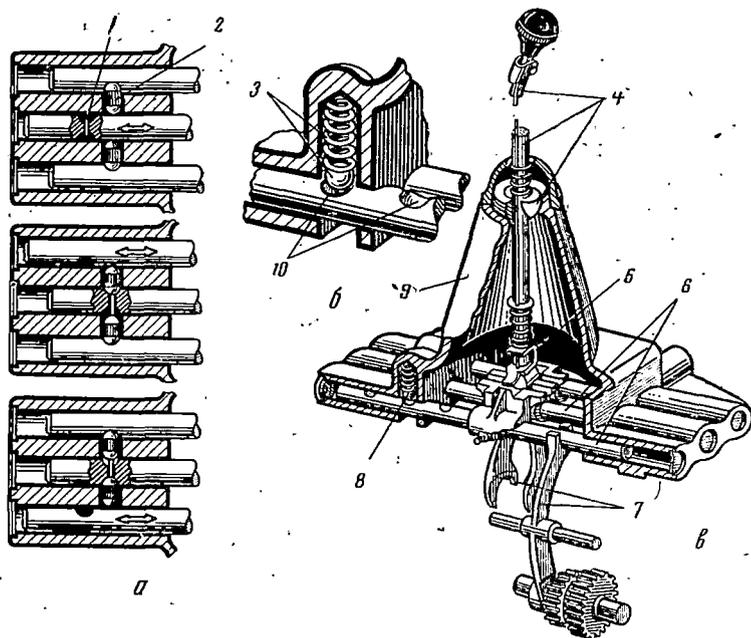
Механизм переключения коробки передач автомобиля ГАЗ-51А:
